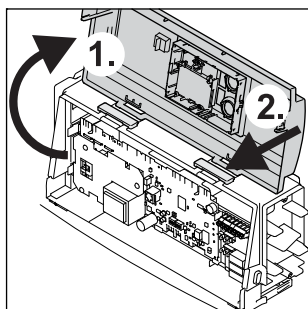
Frontblende öffnen und in Montageposition bringen.
